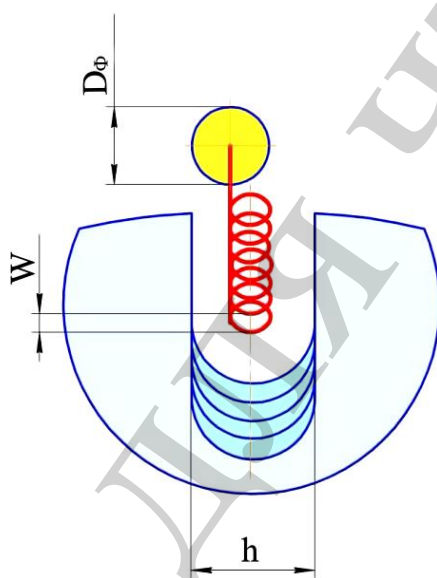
Схема трохоїдального фрезерування вузької канавки
